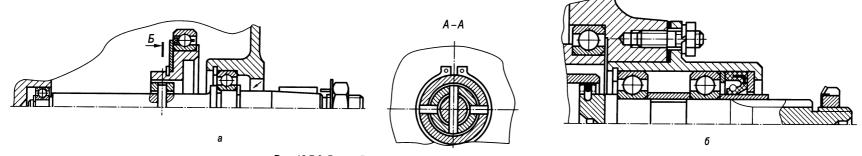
Входной вал волнового (а) и планетарного (б) зубчатого редуктора
